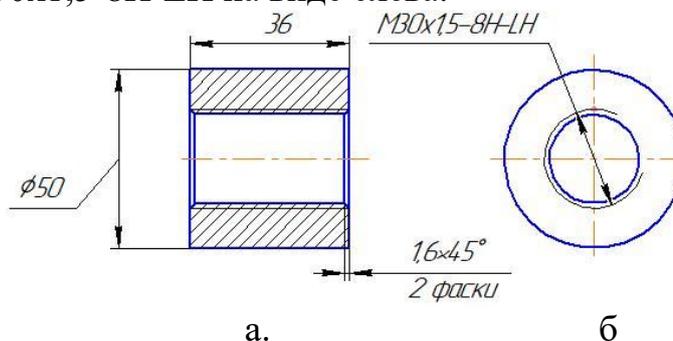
Фрагмент детали втулка с обозначенным размером внутренней метрической резьбы (вид б).
